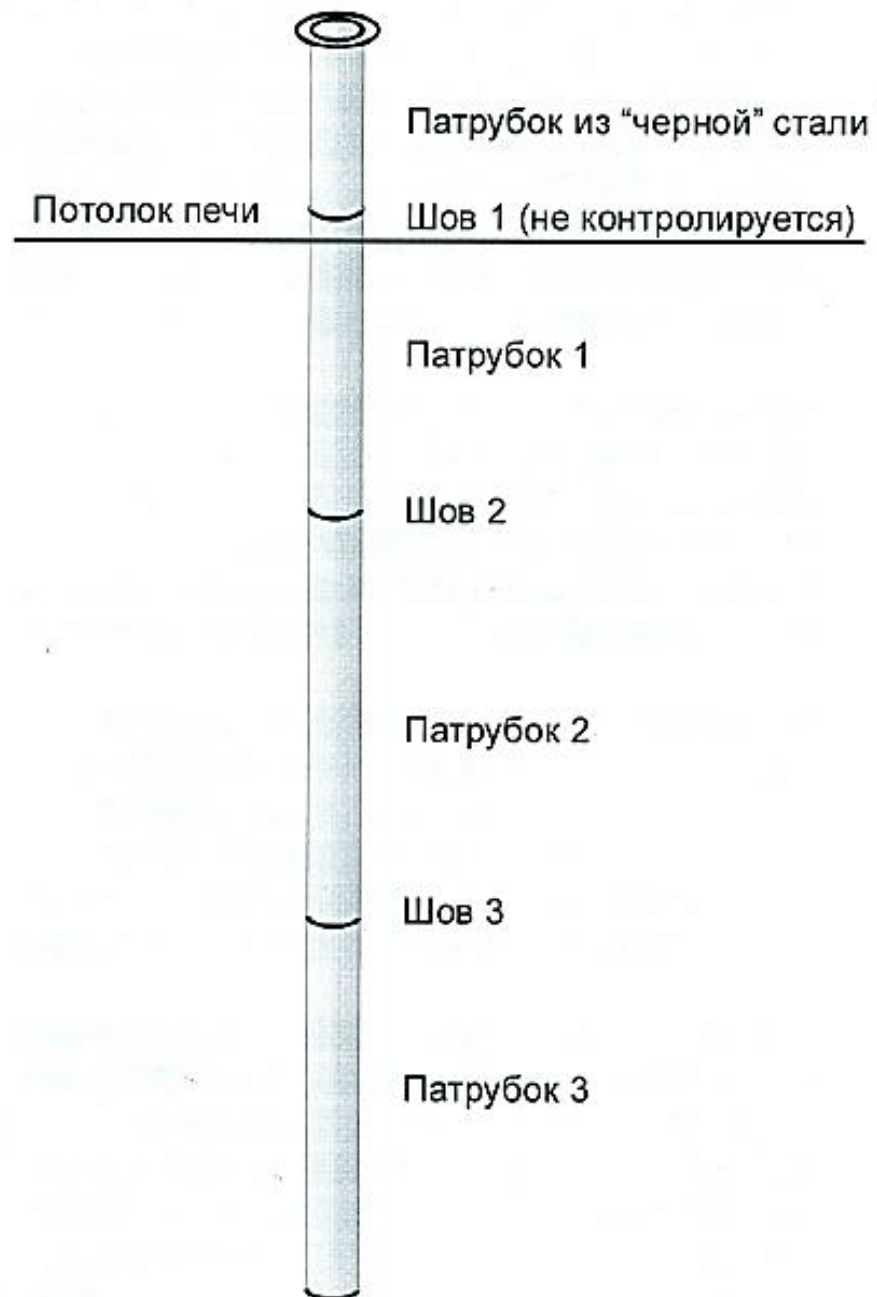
Нумерация сварных швов и патрубков реакционных труб печи риформинга
